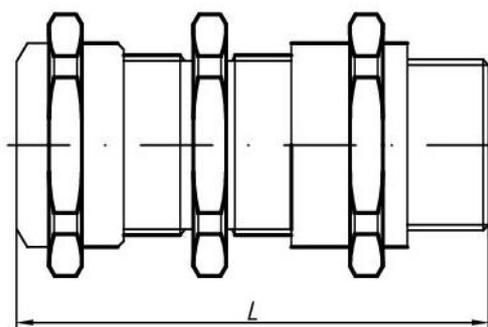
Кабельный ввод КНН для монтажа открытой прокладки кабеля,
